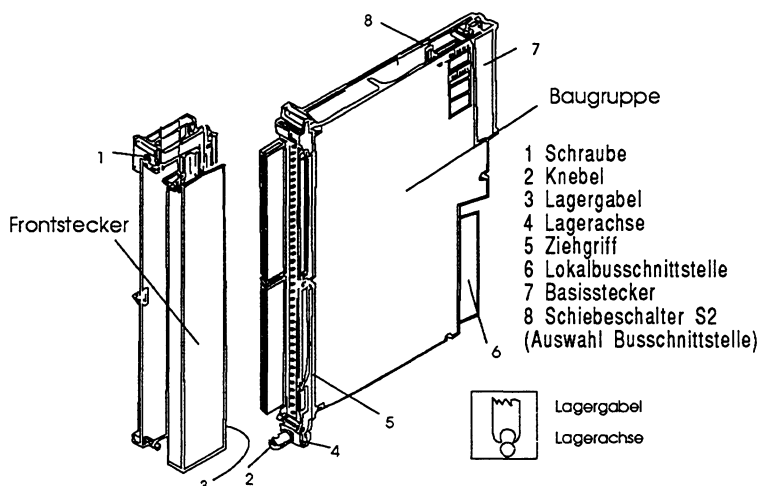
Baugruppe mit 20 mm Einbaubreite und Frontstecker mit Crimpkontakten
